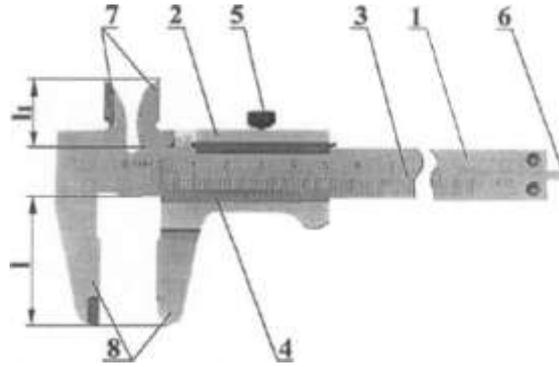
Устройство штангенциркуля ШЦ-1-125-0,1-1
